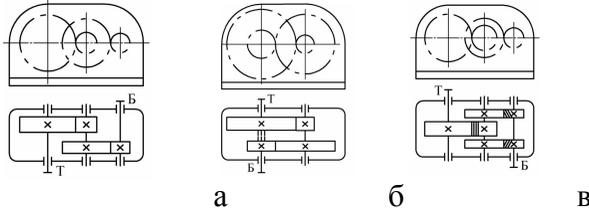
Кинематические схемы двухступенчатых цилиндрических редукторов: а – выполненный по развернутой схеме; б – соосный; в – с раздвоенной быстроходной ступенью;
